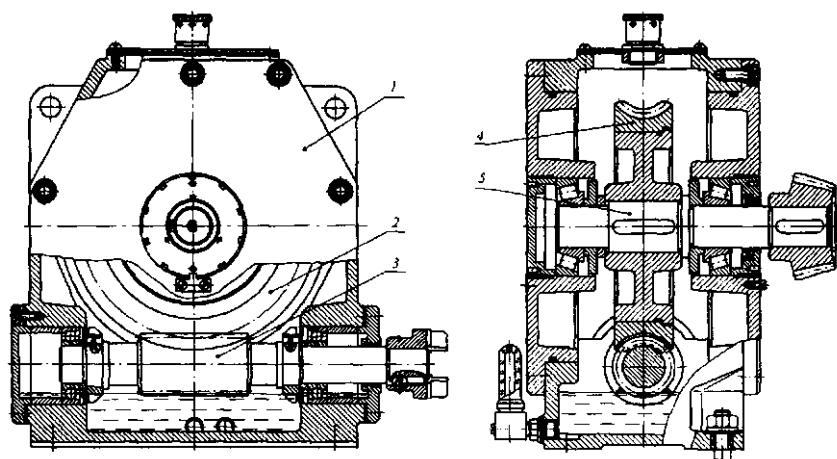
Редуктор червячный, одноступенчатый с нижним расположением червяка: 1 — корпус редуктора; 2 — червячное колесо; 3 — червяк; 4 — зубчатый венец червячного колеса, 5 — вал червячного колеса
